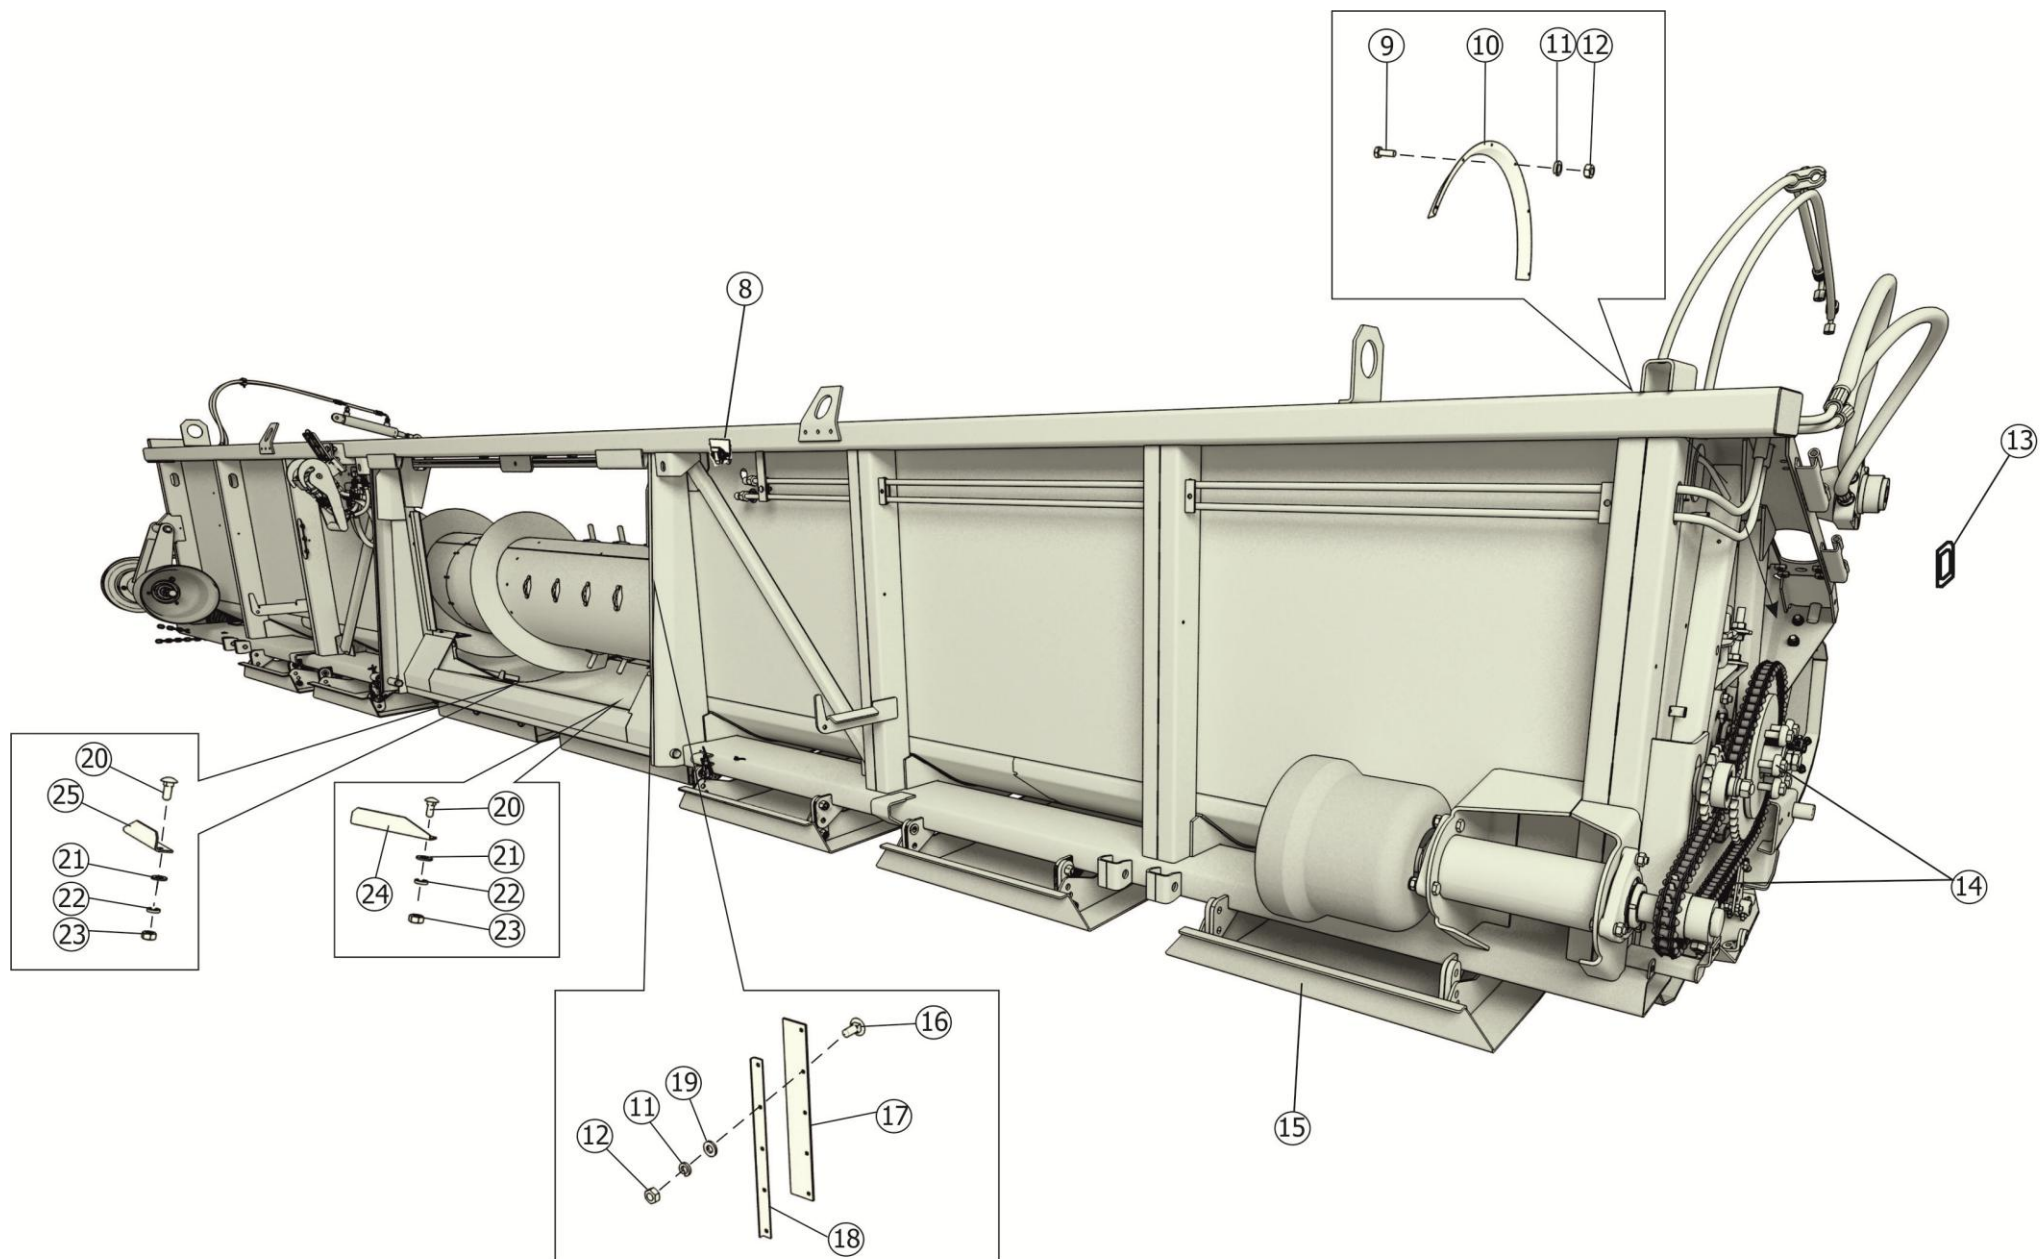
Корпус ЖСУ-703.01.00.000
